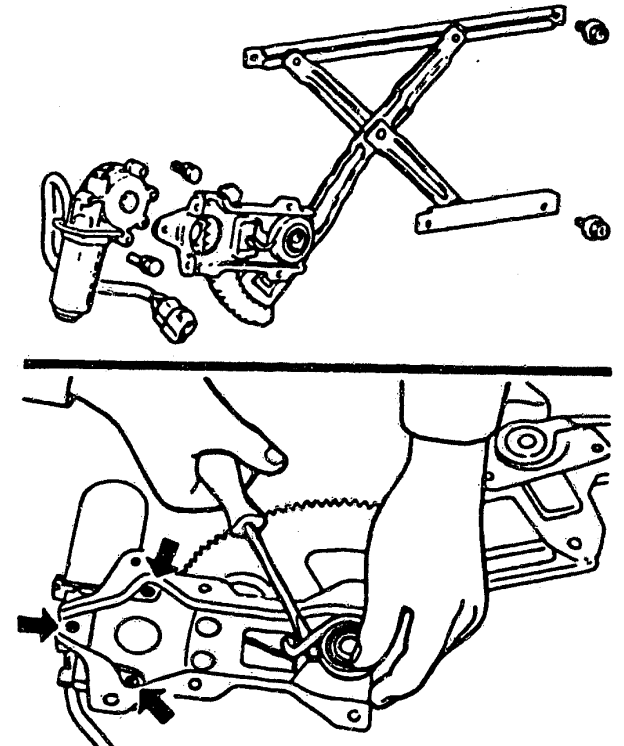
Motor und Gestänge des elektrischen Scheibenhebers. Beim Lösen des Motors (unten) ist darauf zu achten, dass der Hebearm wegen der gespannten Feder hochspringen kann!
